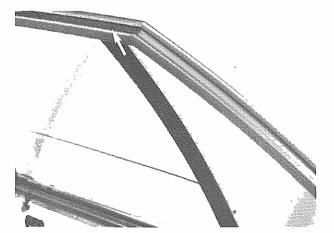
Vite fissaggio superiore guida vetro Glass guide upper fixing screw
